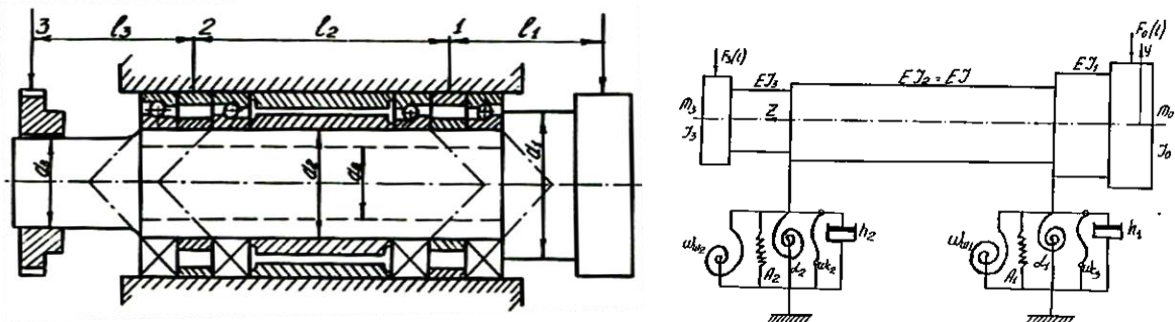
Шпиндельний вузол: конструктивна та розрахункова схеми
